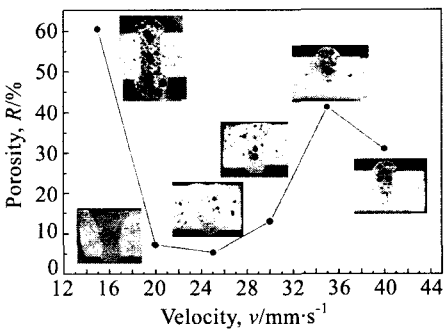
焊接速度对 AM50A 激光焊缝气孔率的影响
